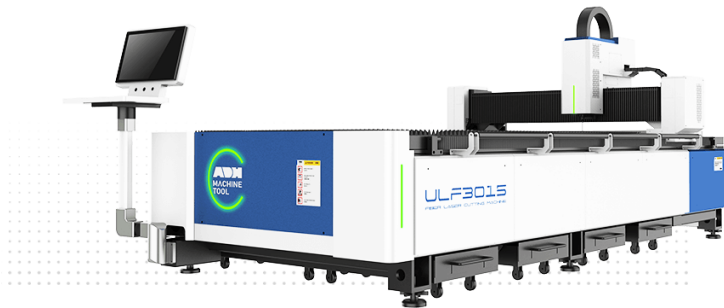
Màquina de tall per làser UFL de ADH Machine. [16]
